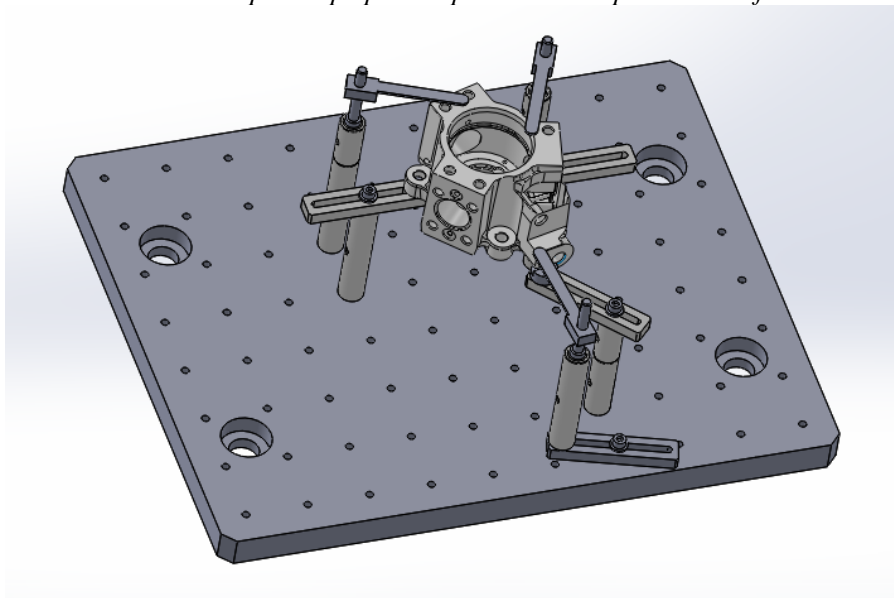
Konstrukční části zajišťující základní polohování komponenty
